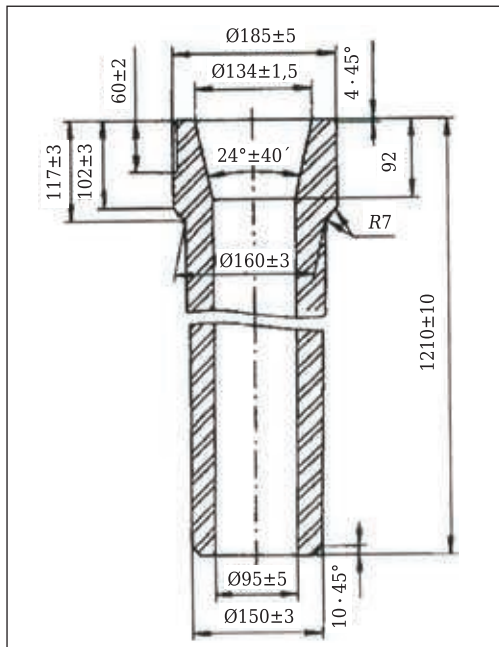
Кварцевая защитная труба марки ТКСБ-38.05 для разливки стали
